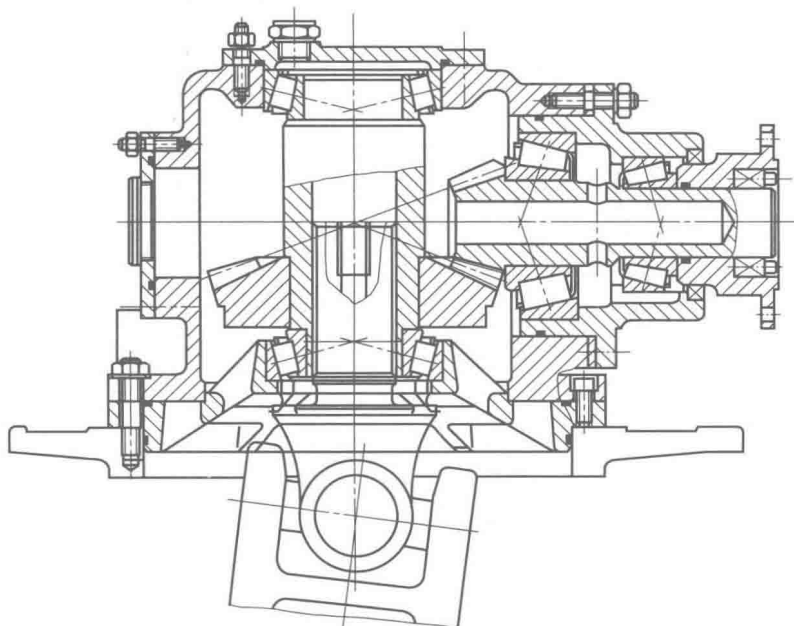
汽艇垂直轴锥齿轮减速箱装配图
